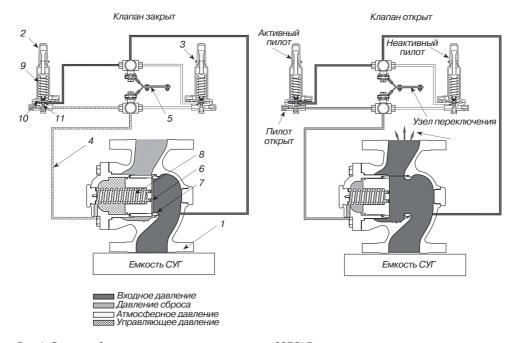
Схема работы предохранительного клапана 63EGLP: 1 — корпус; 2 — активный пилот; 3 — неактивный пилот; 4 — соединительные трубопроводы; 5 — узел переключения; 6 — рабочий клапан; 7 — седло рабочего клапана; 8 — управляющая пружина; 9 — пружина; 10 — мембрана; 11 — клапан
